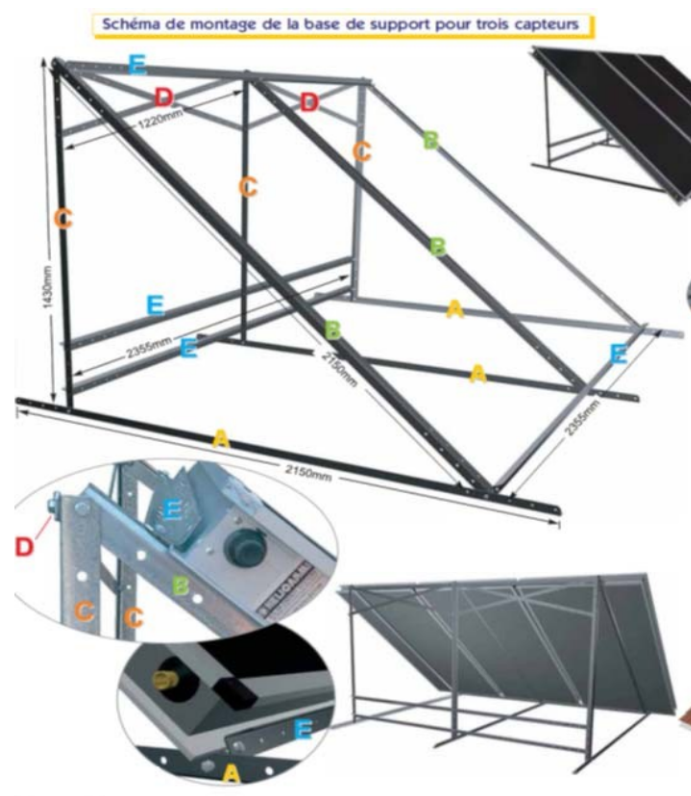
Système de montage – montage sur support horizontal 3 capteurs
